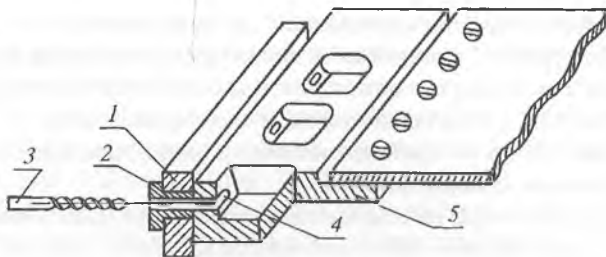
Сверление отверстий по кондуктору: 1 — кондуктор; 2 — кондукторная втулка; 3 — сверло; 4 — отверстие под стыковой болт (ОСВ); 5 — стыковой узел панели
